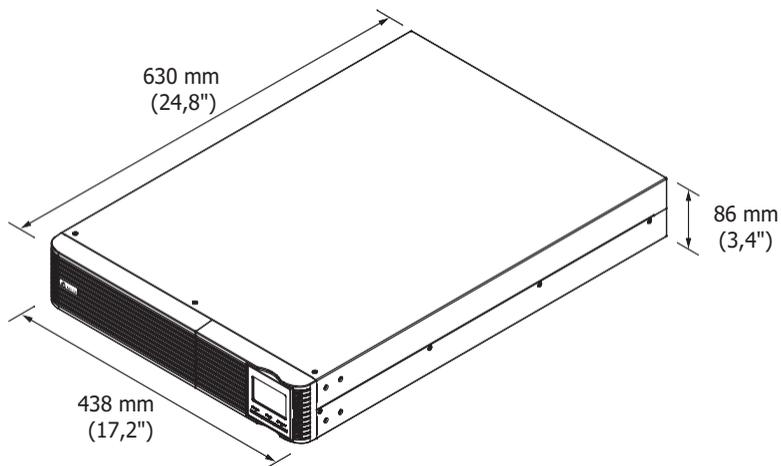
Exterior e Dimensões_ 1kVA)
